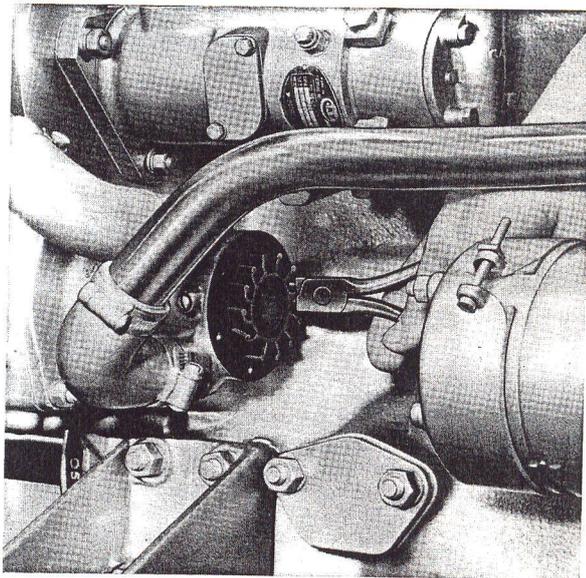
Dépose du rotor de la pompe à eau de mer.
